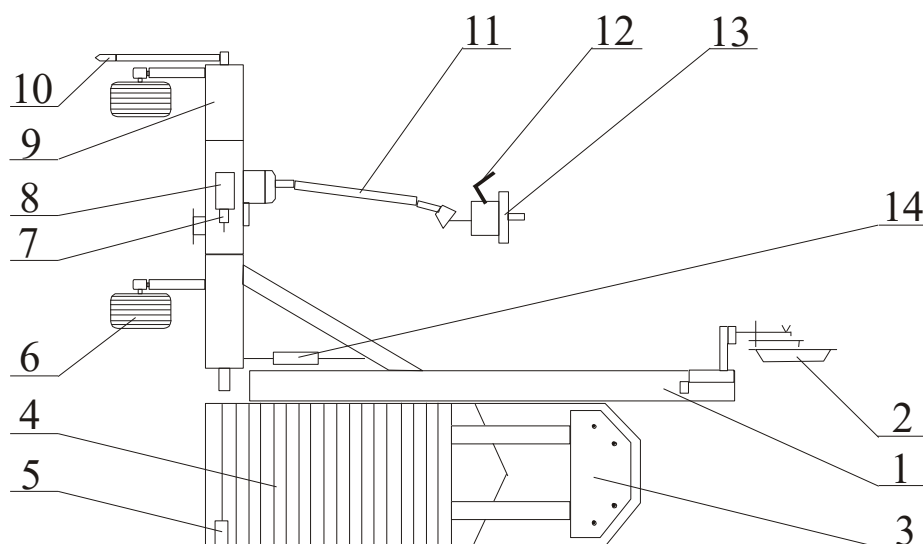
Схема АВС-0,6: 1 - подільний брус; 2 - металеве колесо з дисковим ножом; 3 - викопувальна скоба; 4 - прутковий транспортер; 5 - вал транспортера; 6 - опорне пневматичне колесо; 7 - запобіжуча муфта; 8 - конусний редуктор; 9 - поперечний брус; 10 - черенковий ніж; 11 - кардана передача; 12 - циліндричний редуктор; 13 - механізм включення транспортера; 14 - гідроциліндр
